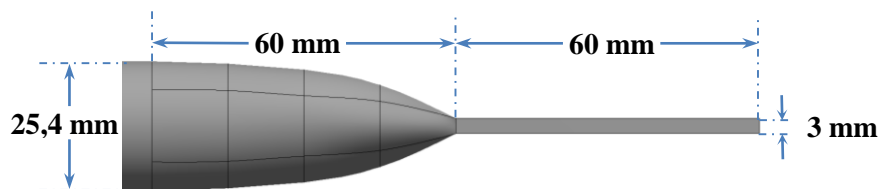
Detalhe da ponta do banzo (Perfil)
